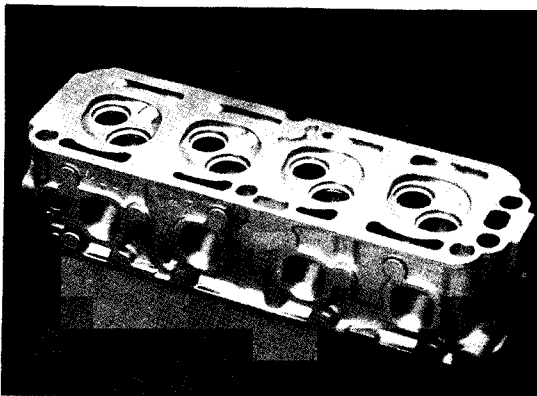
Metallic mold-cast cylinder head for private car. (weight : 6.6kg)
